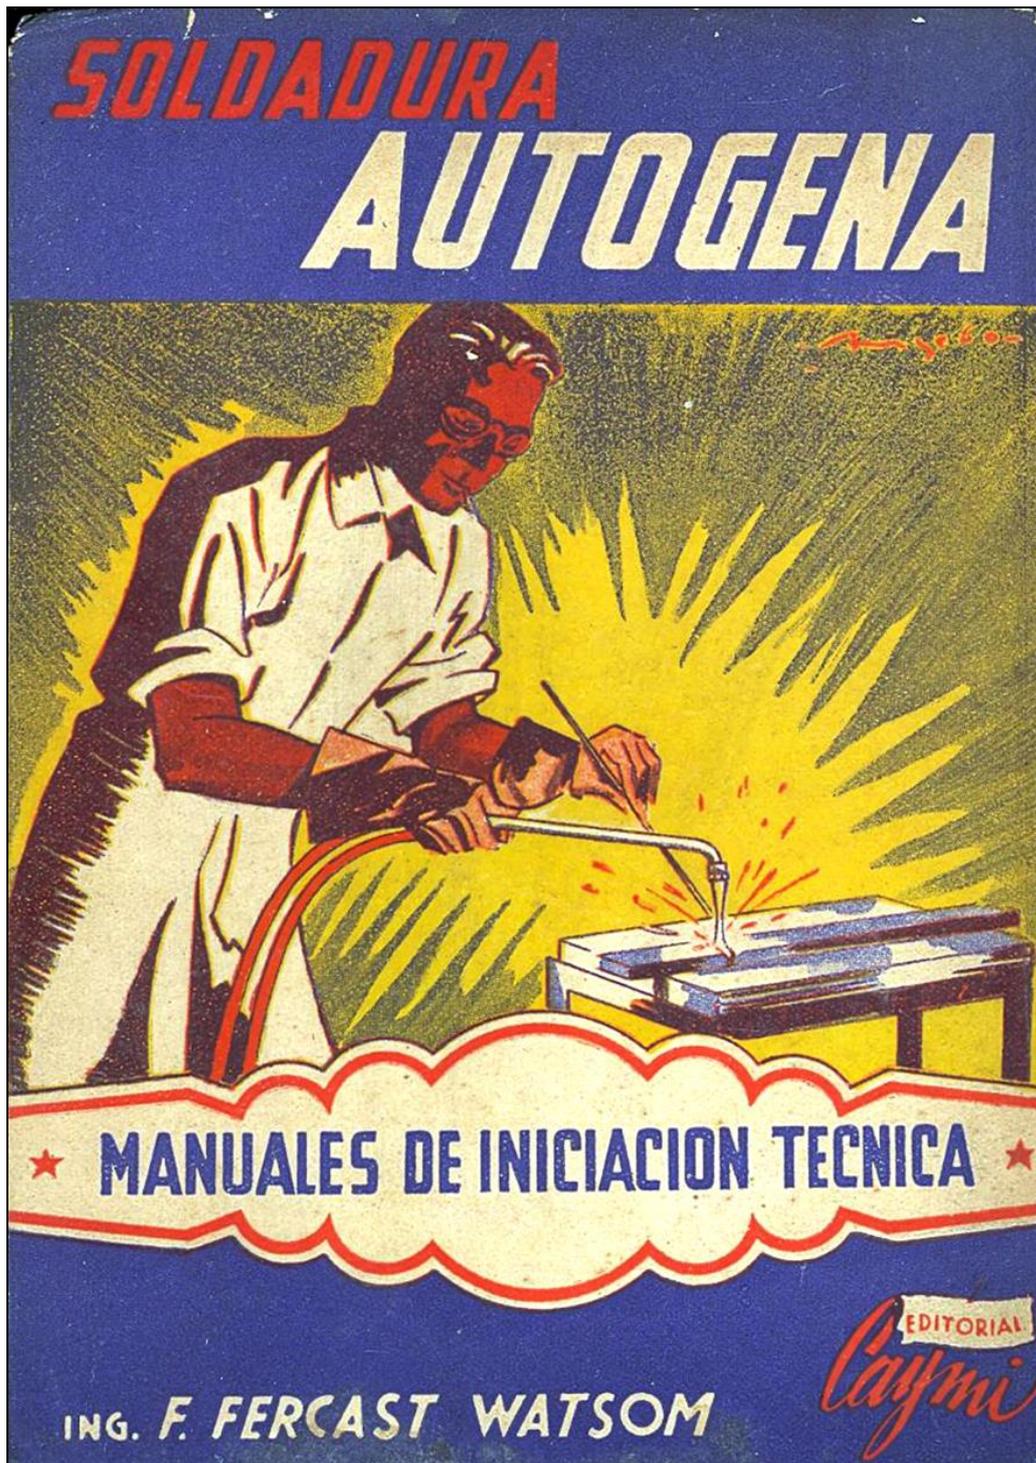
Portada de un libro sobre soldadura autógena (Arch. J.M. Sanchis)
